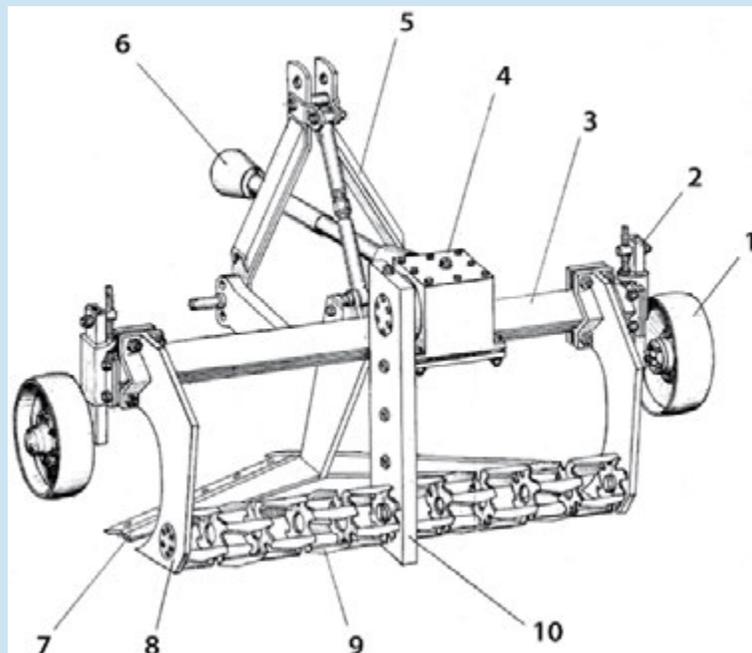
Схема комбинированного подпокровного фрезерователя:
